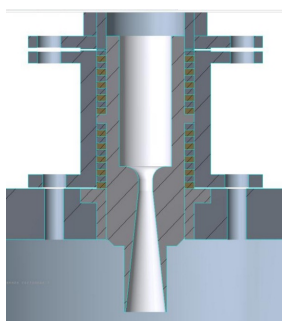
Способ закрепления сопла в корпусе струйного аппарата эжектора
